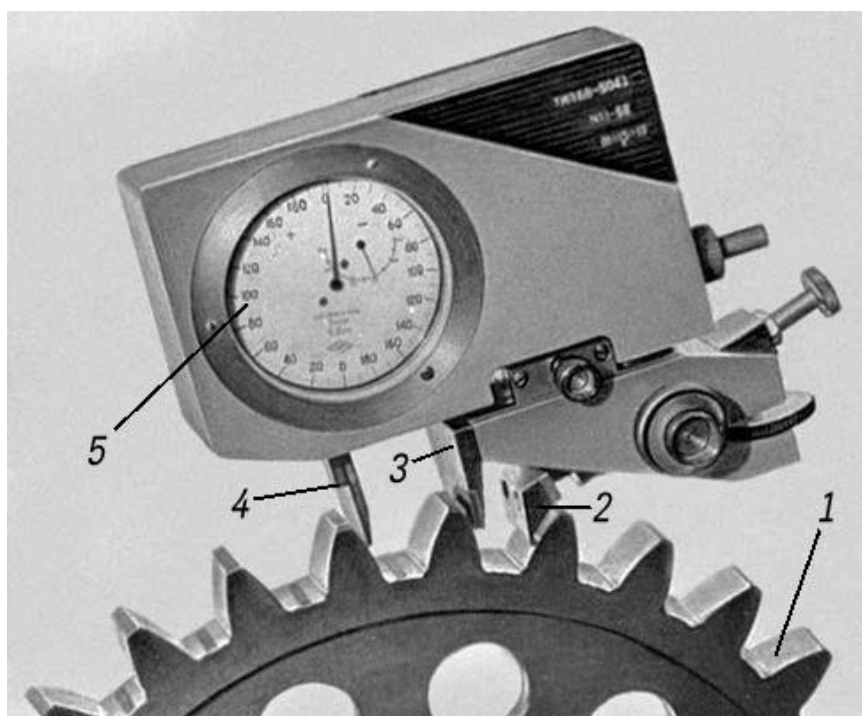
Отечественный накладной шагомер для контроля шага зацепления цилиндрических зубчатых колёс с модулем зацепления $m=1,5—10$ мм:
